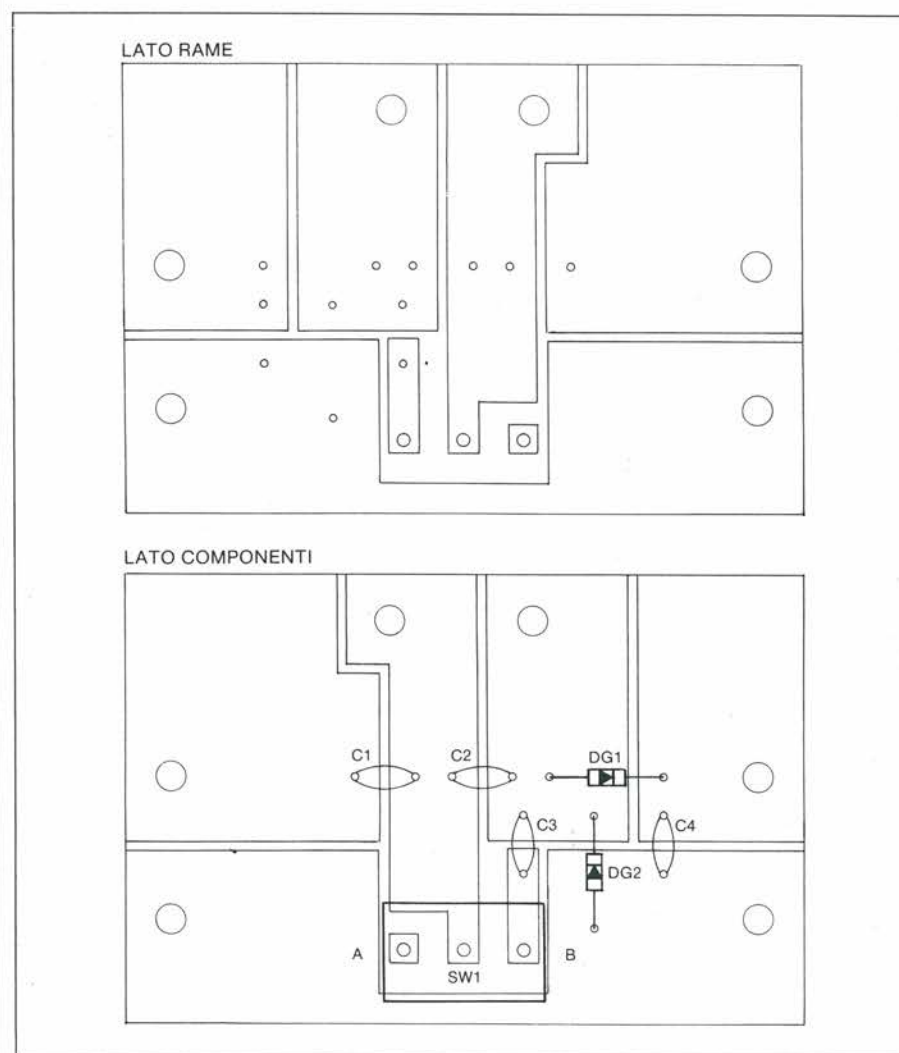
Il circuito stampato, lato rame e lato componenti.
